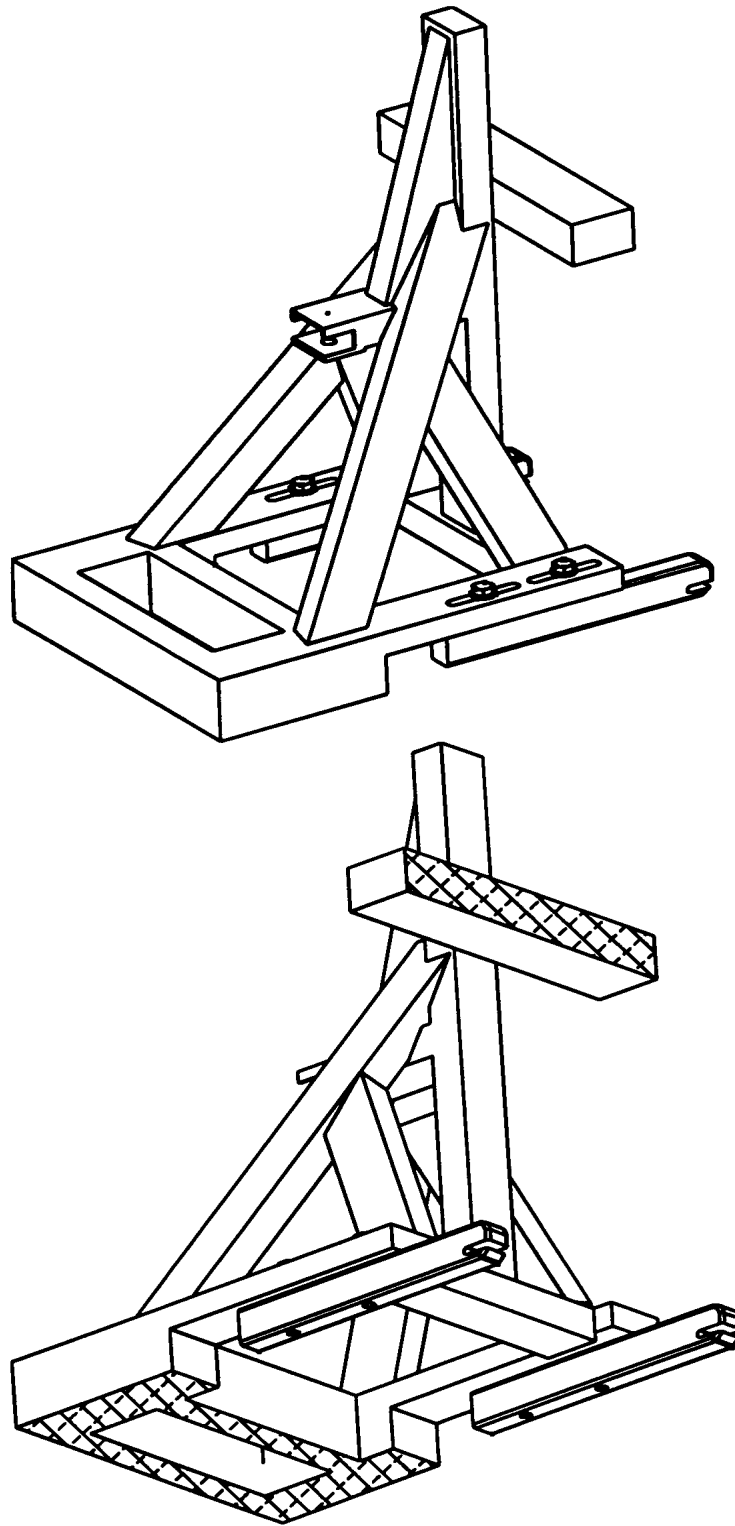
Vues schématiques tridimensionnelles du dispositif d'essai d'application de la force statique ISO-13216-1
